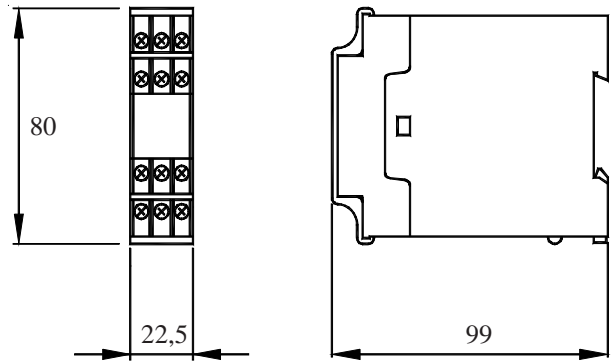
Abmessung des Steuergerätes PRSU/2 (in mm)
